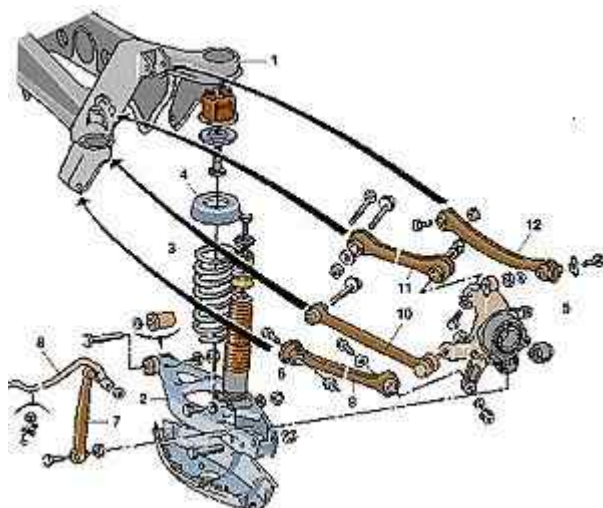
Детали задней подвески моделей W124 и W201: 1 – подрамник; 2 – нижний поперечный рычаг; 3 – пружина подвески; 4 – верхняя опорная чашка пружины; 5 – корпус ступицы; 6 – амортизатор; 7 – соединительная тяга; 8 – стабилизатор поперечной устойчивости; 9 – нижний наклонный рычаг; 10 – толкающий рычаг; 11 – растяжка верхнего рычага; 12 – верхний рычаг.
